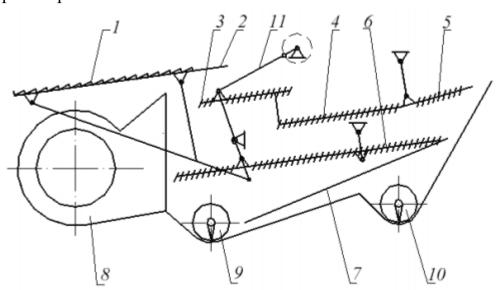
Схема очистки зерноуборочного комбайна КЗС-10К: 1 — стрясная доска; 2 — пальцевая решетка; 3 — дополнительное решето; 4 — верхний решетный стан; 5 — удлинитель верхнего решета; 6 — нижний решетный стан; 7 — скатная доска; 8 — вентилятор; 9 — зерновой шнек; 10 — колосовой шнек; 11 — кривошипно-шатунный механизм
